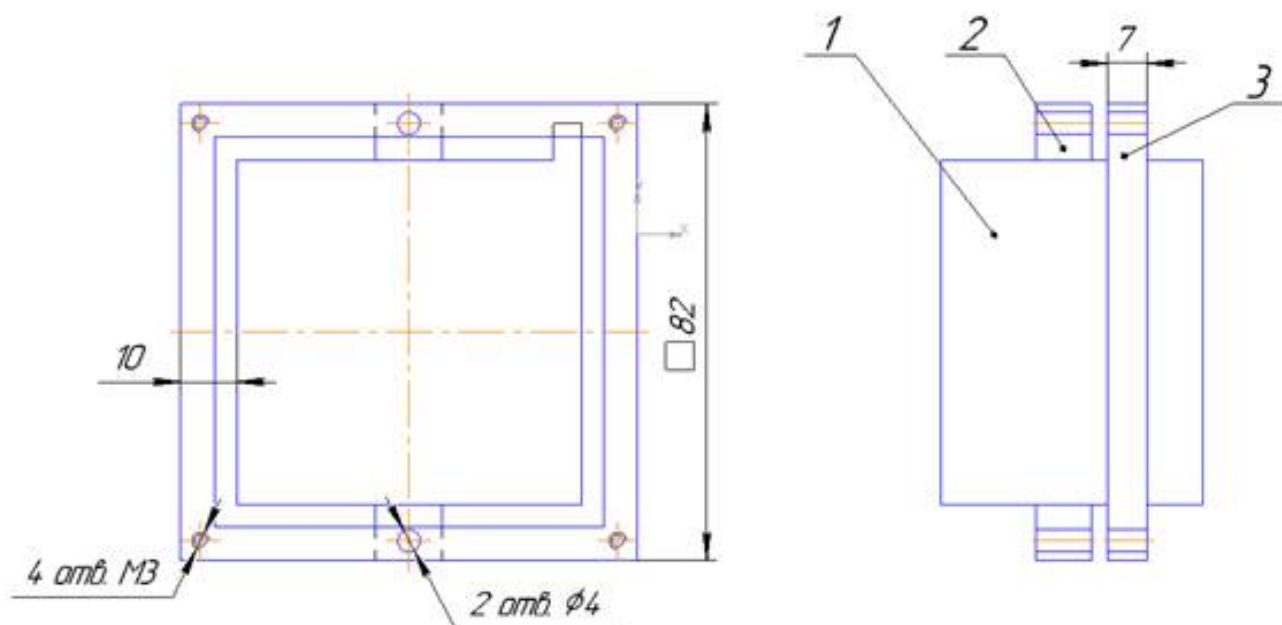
Установка О-образного сердечника трансформатора ТЛМ
